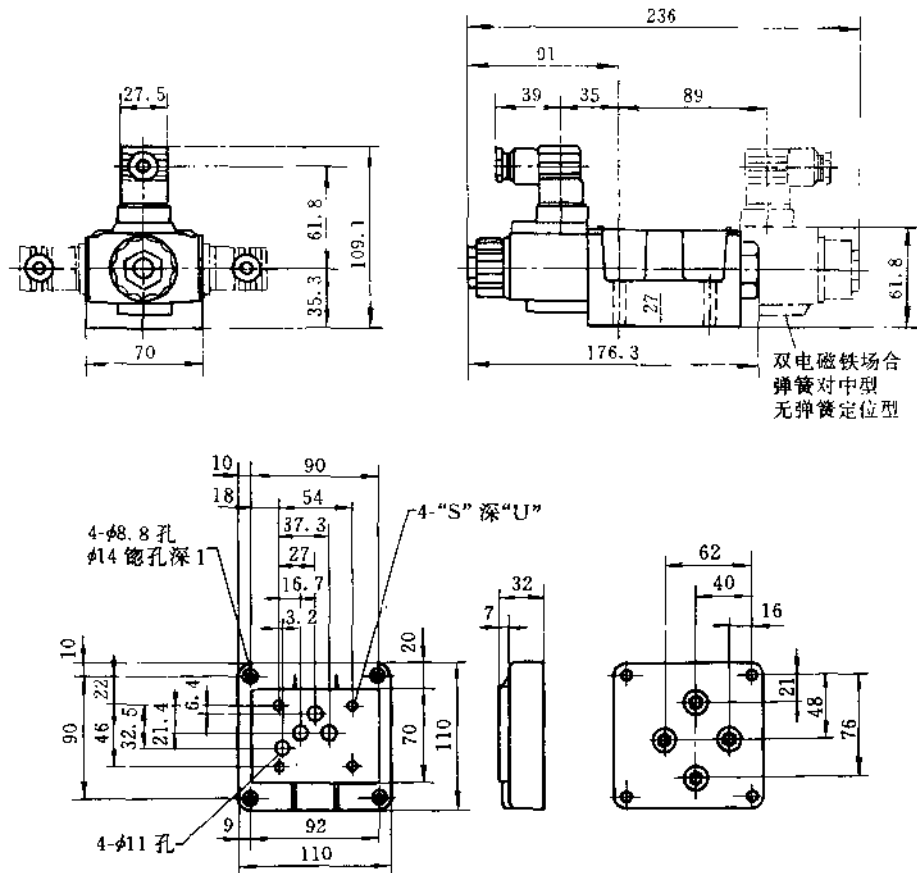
DSG-03 型电磁换向阀外形及连接尺寸图
